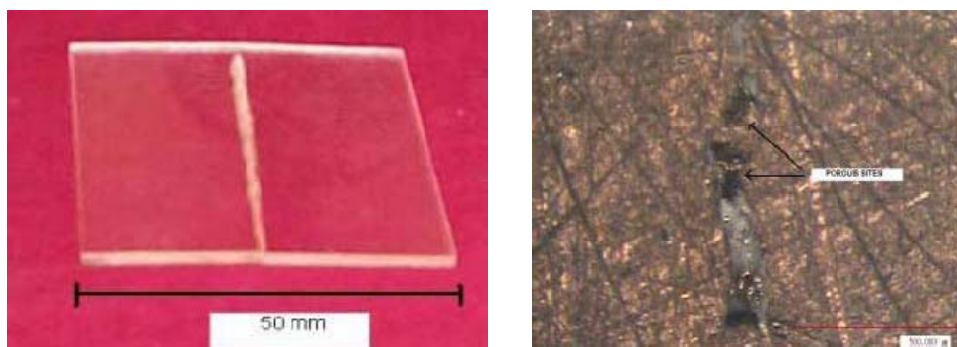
Typische Verbindung bei „Frictional Vibration Welding“[25 S. 5]
